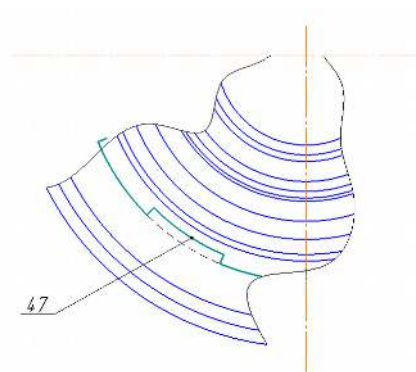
Эскиз детали «Корпус топливно-пусковой системы» с пронумерованными поверхностями
